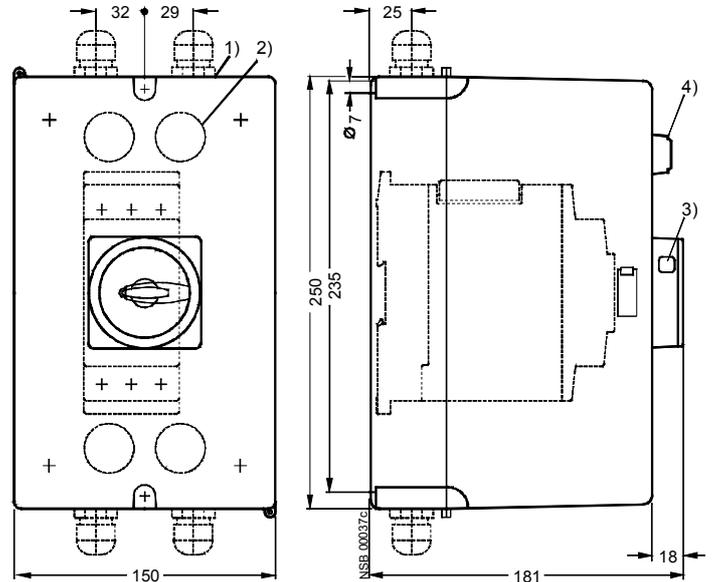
3RV19 33-1.... (für Baugröße S2)
